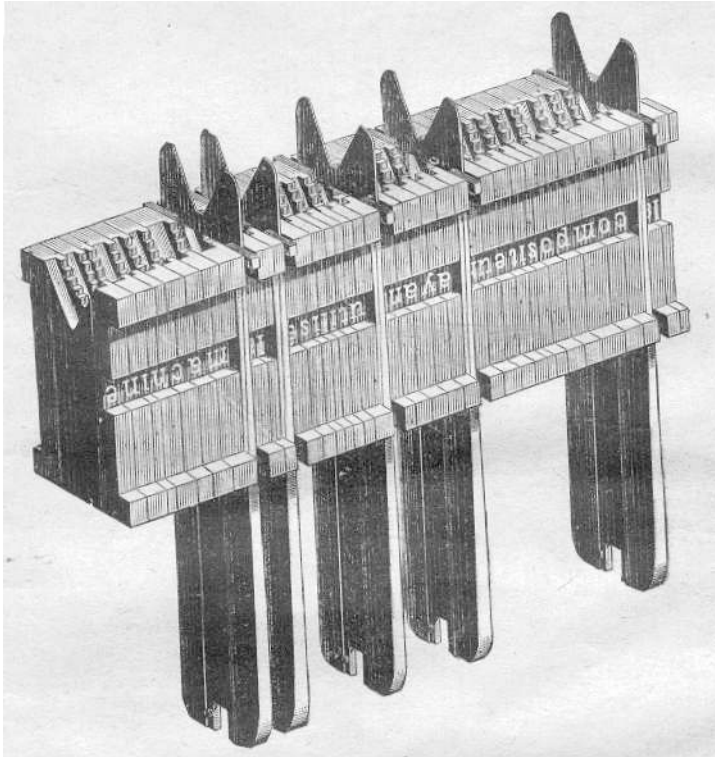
Matrices et espaces assemblés pour servir de fond de moule pour la fabrication d’une ligne au plomb
